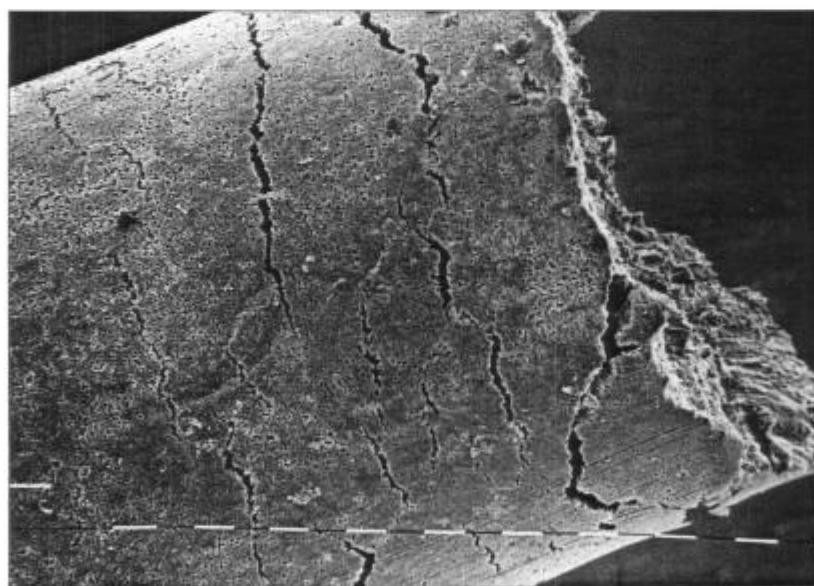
Fisuras y picaduras en la superficie lateral de un alambre de Zry-4 traccionado
